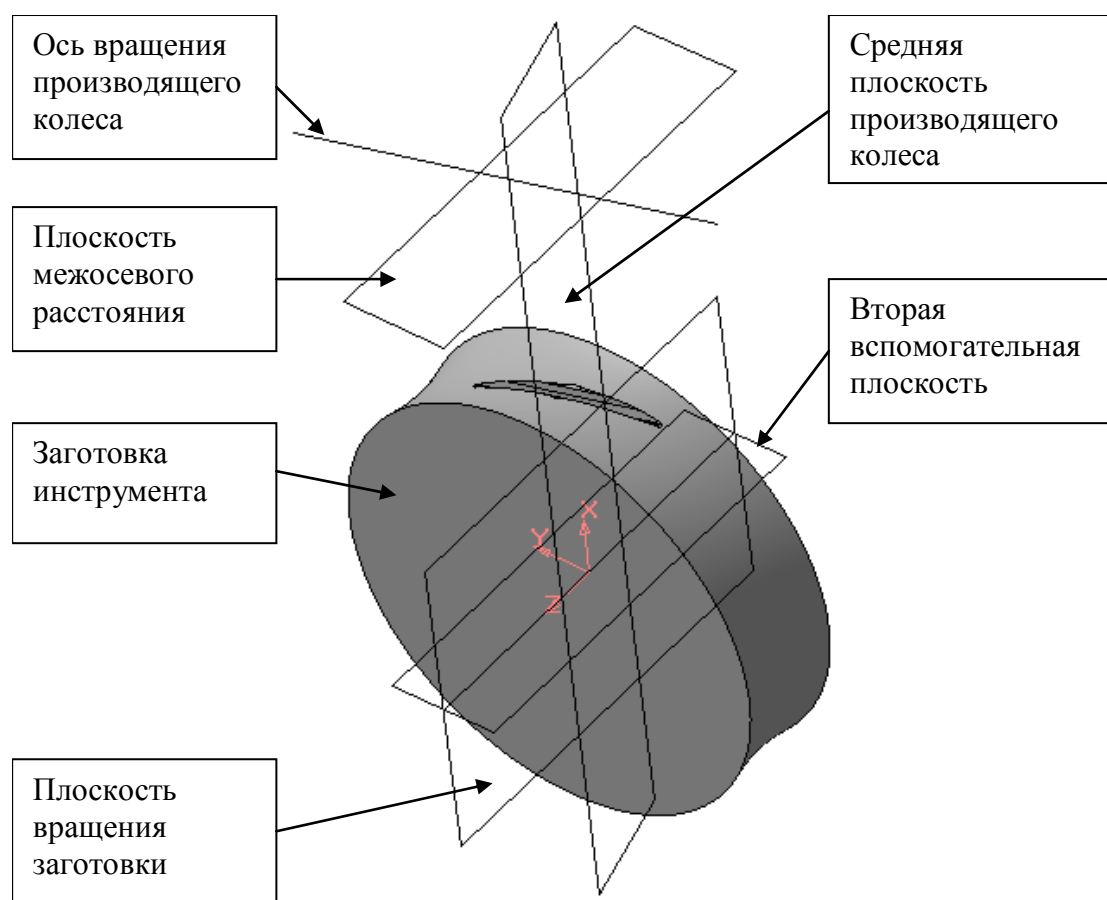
Заготовка инструмента с вспомогательными построениями
